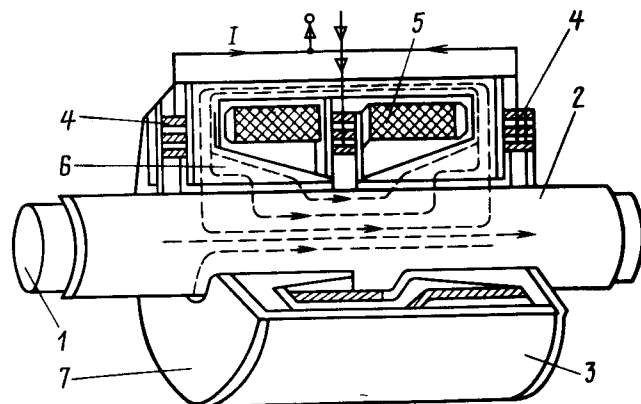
Цилиндрический линейный двигатель постоянного тока
